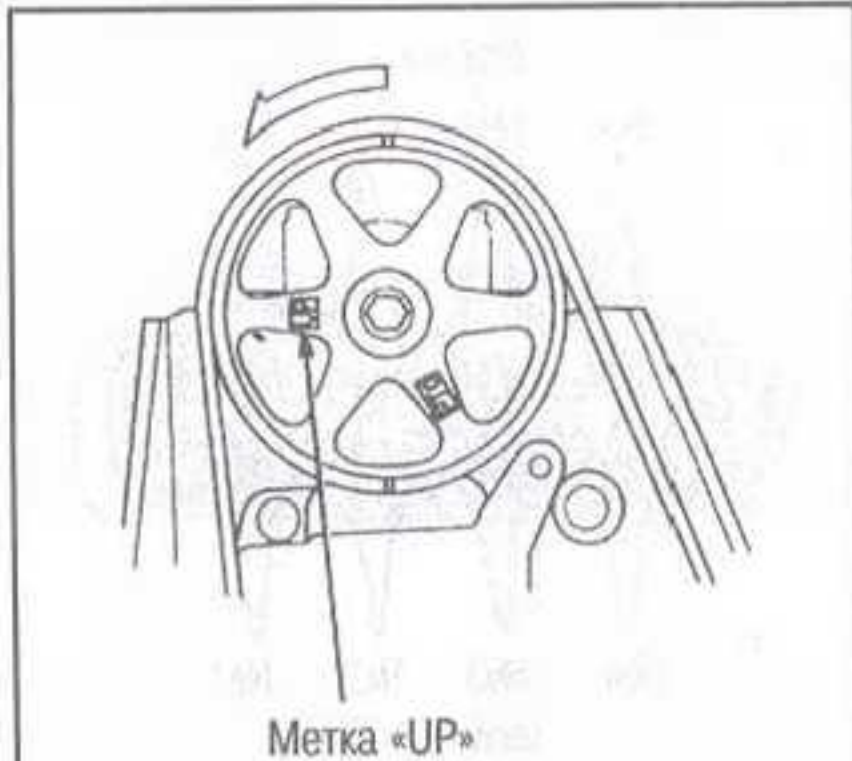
Вращайте коленчатый вал, пока звездочка распределительного вала не установится в положение, показанное на рисунке, при установке поршня цилиндра № 3 в ВМТ в такте сжатия — 4-цилиндровые модели Odyssey
